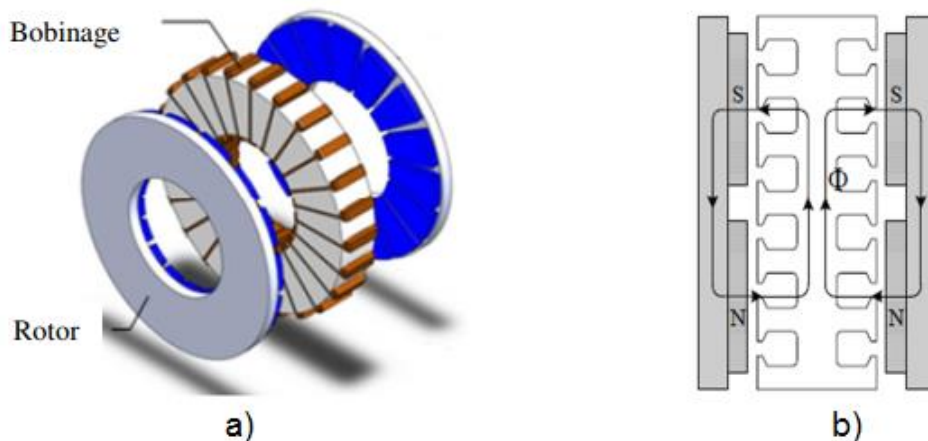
Machine à flux axial stator double rotor a) avec stator encoché et bobinage toroïdal b) type NN [23], [22]
